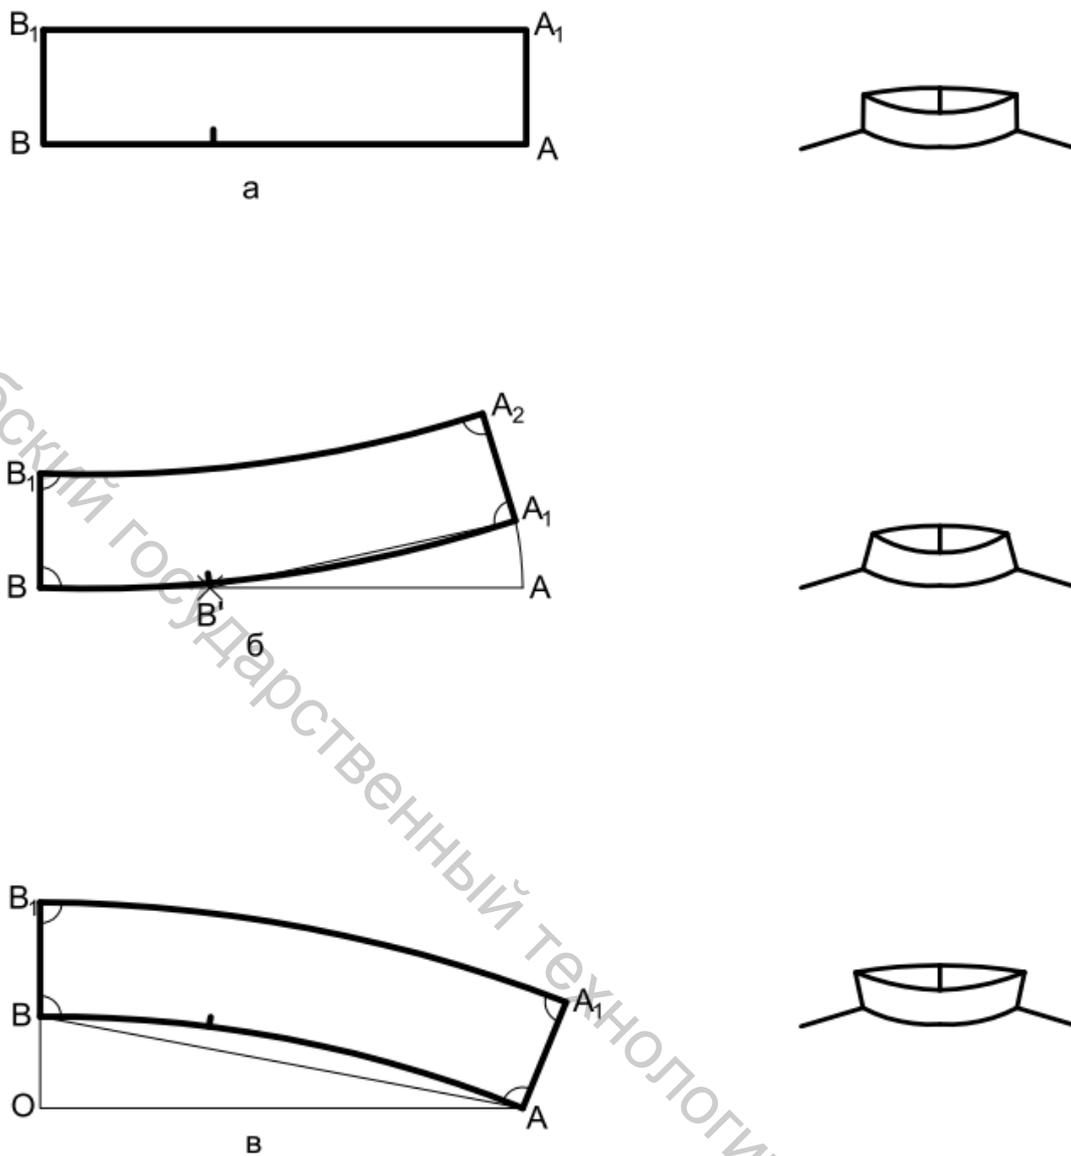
Внешний вид и построение конструкций воротников-стоек: а – цилиндрическая форма; б – коническая форма; в – воронкообразная форма
